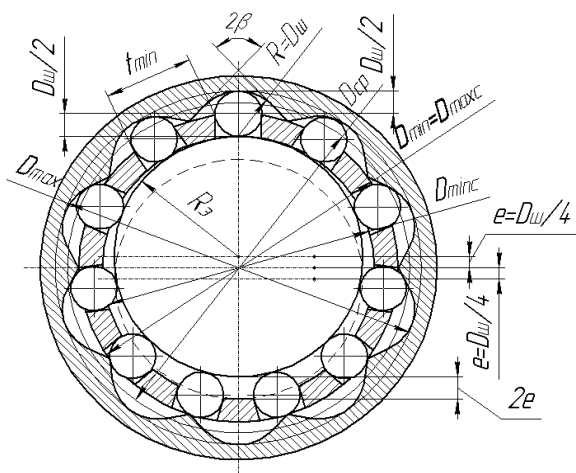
Схема шарикового зацепления с размерами элементов деталей редуктора
